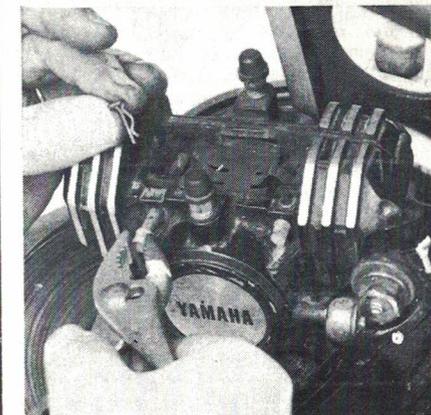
Retrait des goupilles de plaquettes (Photo RMT)
